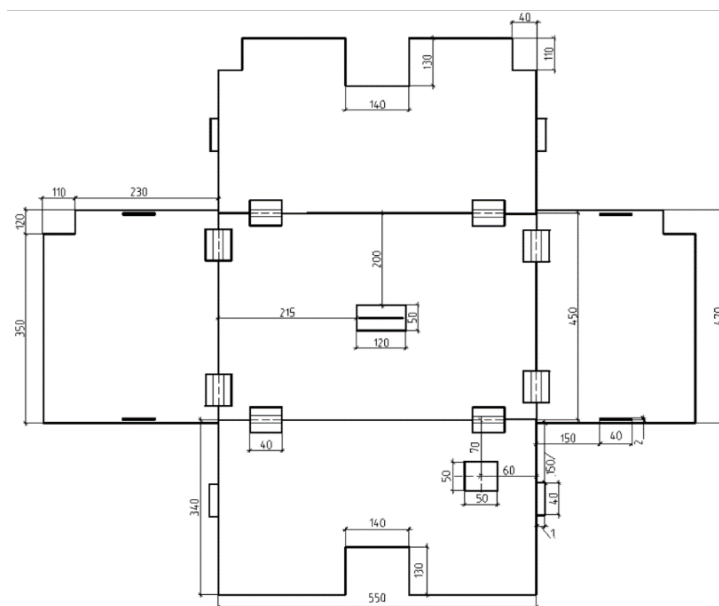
Геометрические размеры металлического корпуса установки «Кожух РТ»
